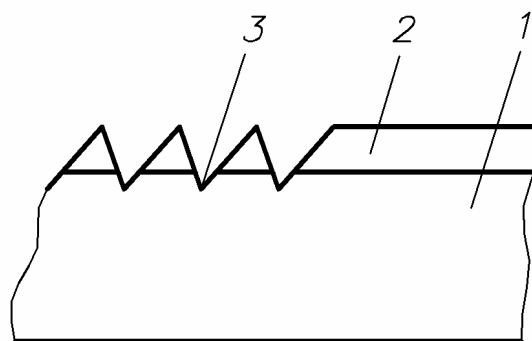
Применение электроннолучевой сварки при изготовлении ленточных пил:
